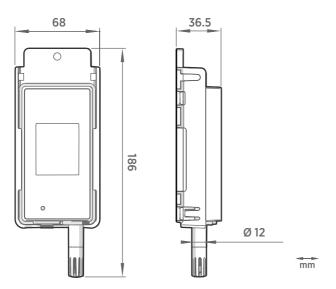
Dimensiones del RFL100 con el soporte de montaje
